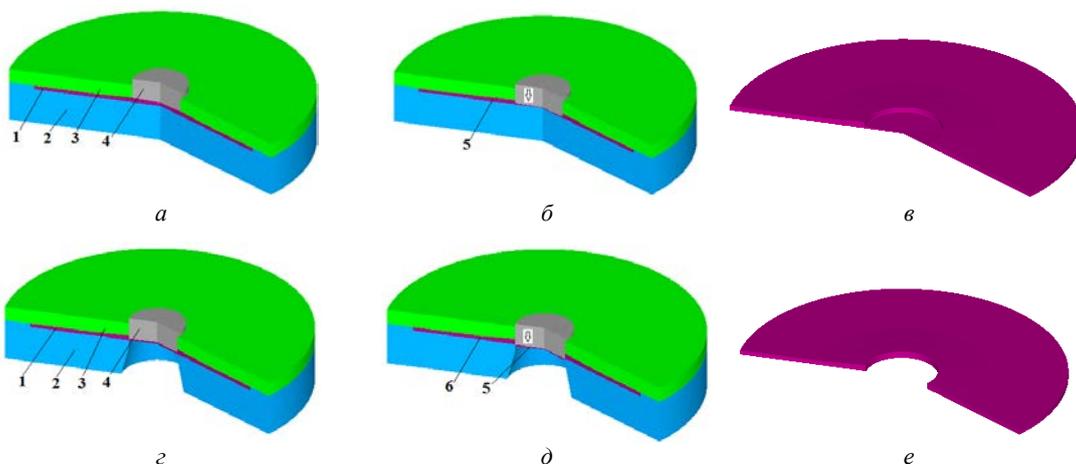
Розрахункові схеми в розрізі при видавллюванні профільованої заготовки з перемичкою та при пробиванні перемички з отриманням профільованої заготовки з отвором: а – схема на початку видавллювання, б – схема в кінці видавллювання, в – профільована заготовка з перемичкою, г – схема на початку пробивання, д – схема в кінці пробивання, е – профільована заготовка з отвором
